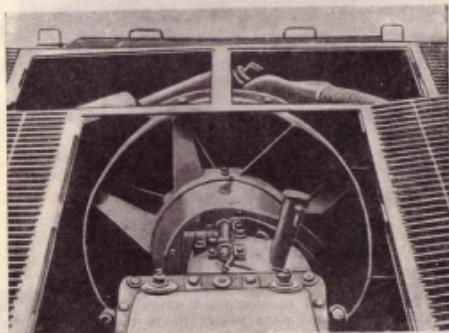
Установка звездообразного мотора Континенталь на колесно-гусеничном танке Т-4.
